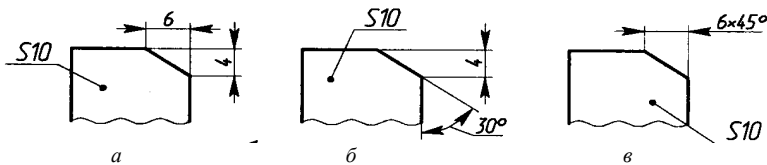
Простановка размеров фасок: *a* – двумя линейными размерами;
